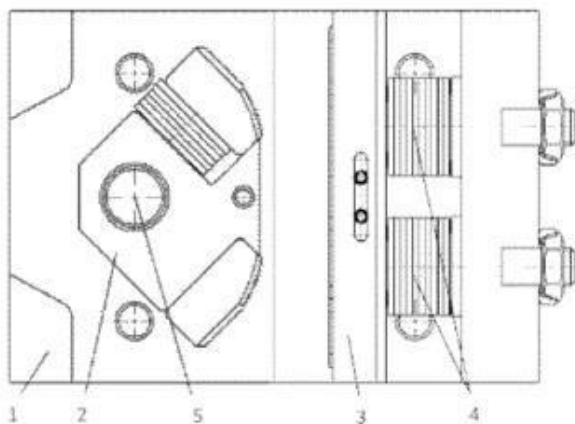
Общий вид ловителя: 1 – корпус, 2 – эксцентриковая защелка, 3 – тормозная колодка, 4 – пакет тарельчатых пружин, 5 – вал
